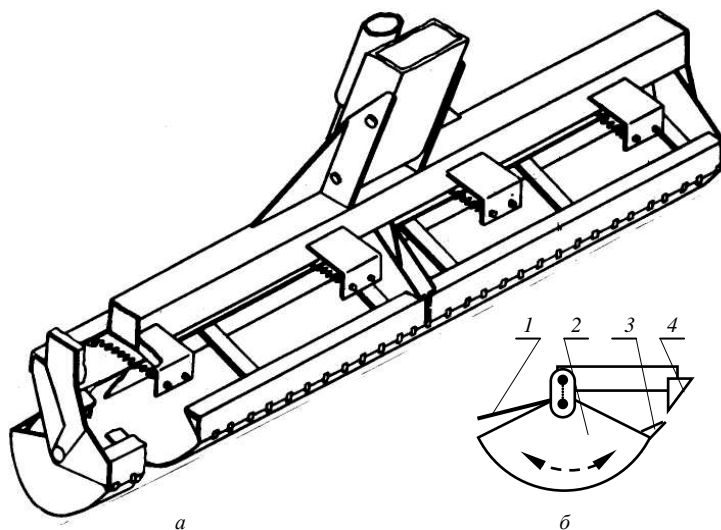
Уширенный поворотный ковш с неподвижной заслонкой и противорежущей кромкой: а – общий вид; б – схема работы;
